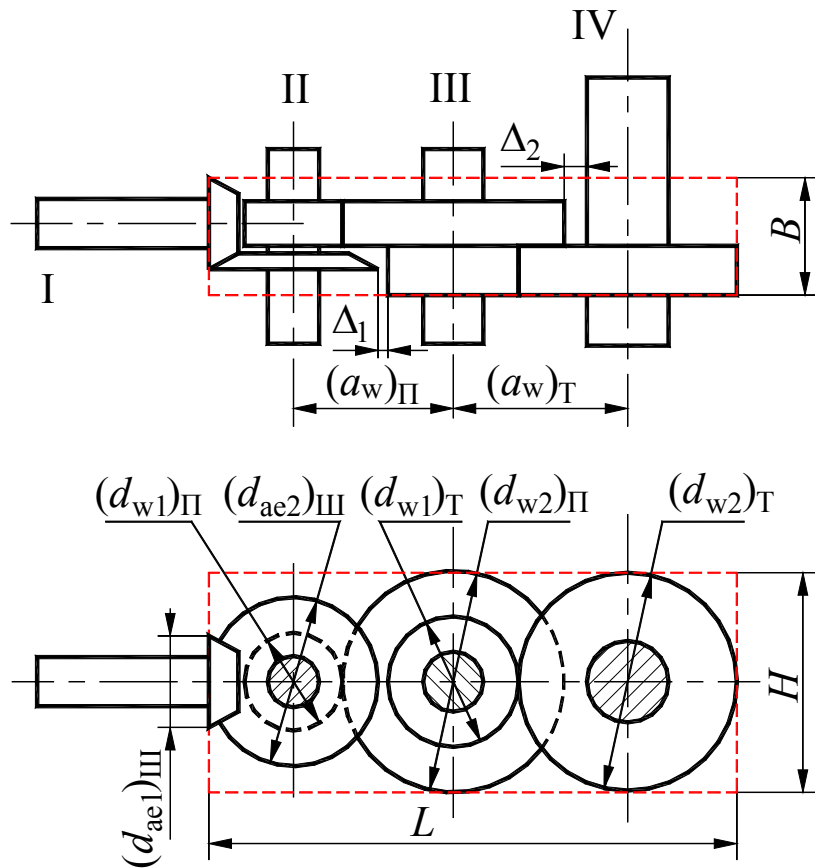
Конічно-циліндричний триступінчастий редуктор
